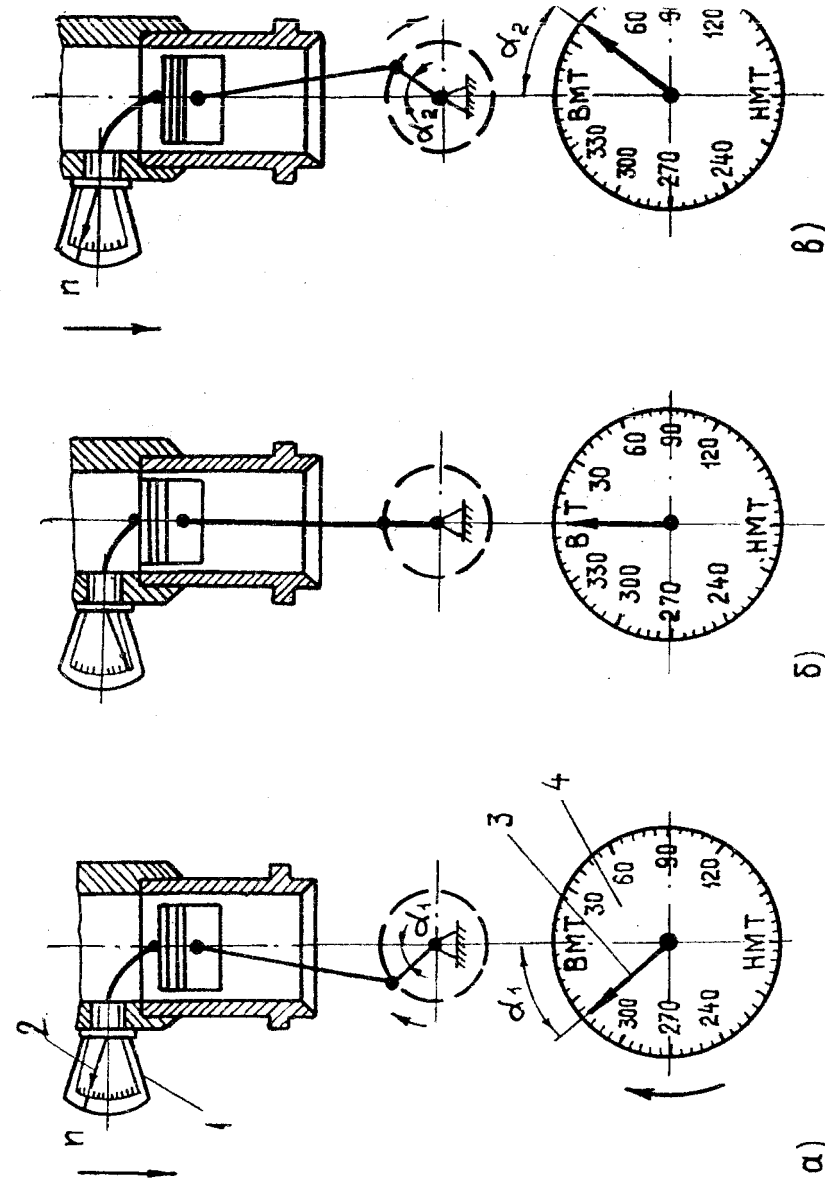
Схема нахождения ВМТ: а-движение поршня вверх; б-ВМТ; в-движение поршня вниз; 1-репляж; 2-указатель репляжа; 3-стрелка-указатель регулировочного диска; 4-регулирующий диск
